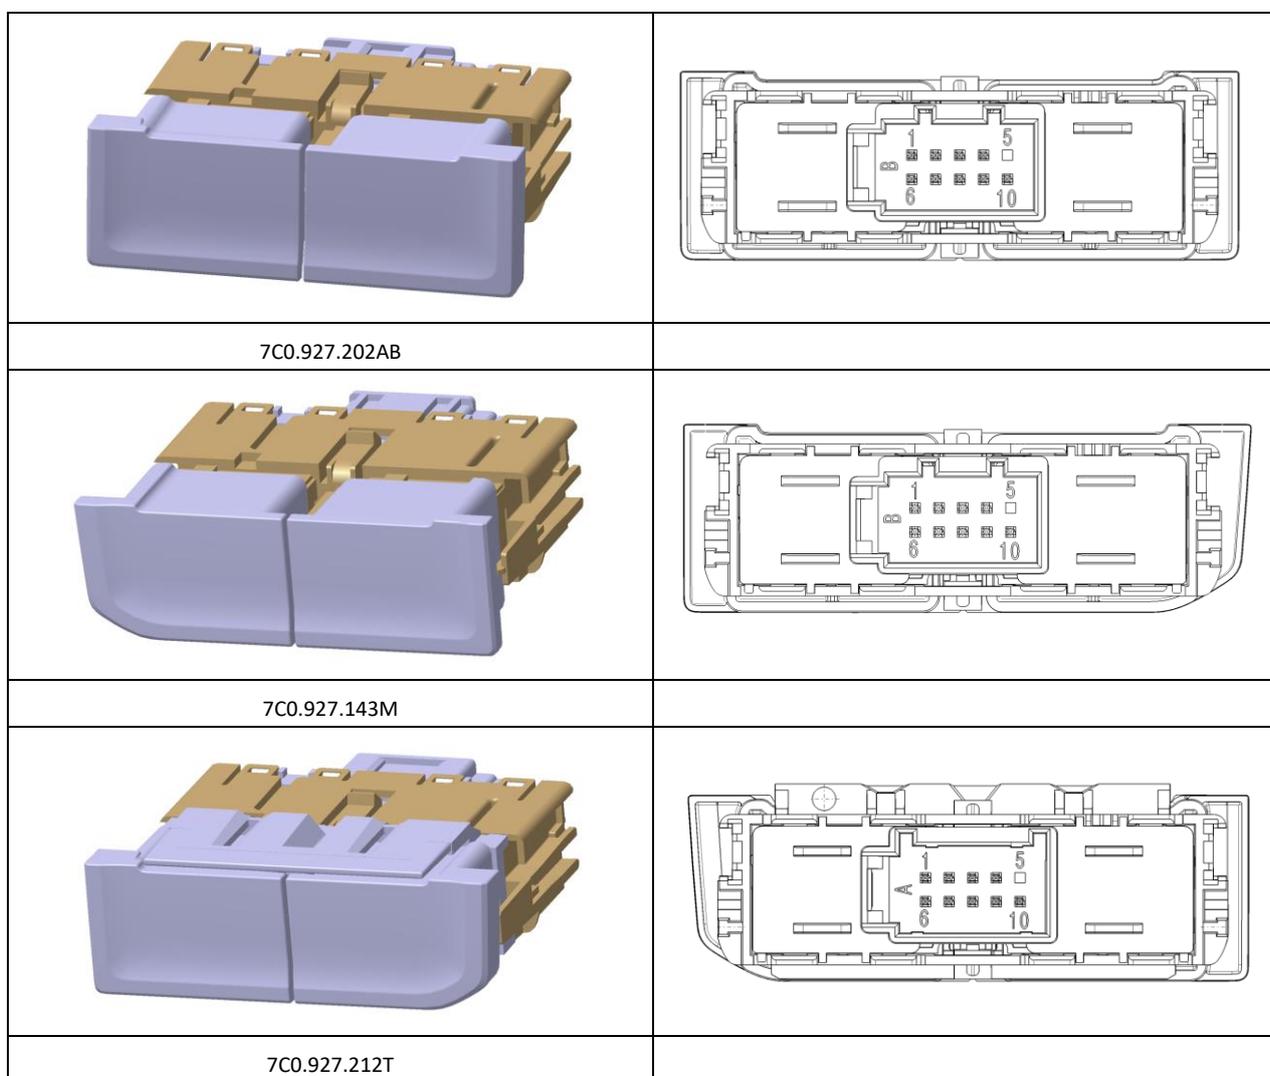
modules de touches vierges disponibles, vue de face et vue arrière avec raccords
